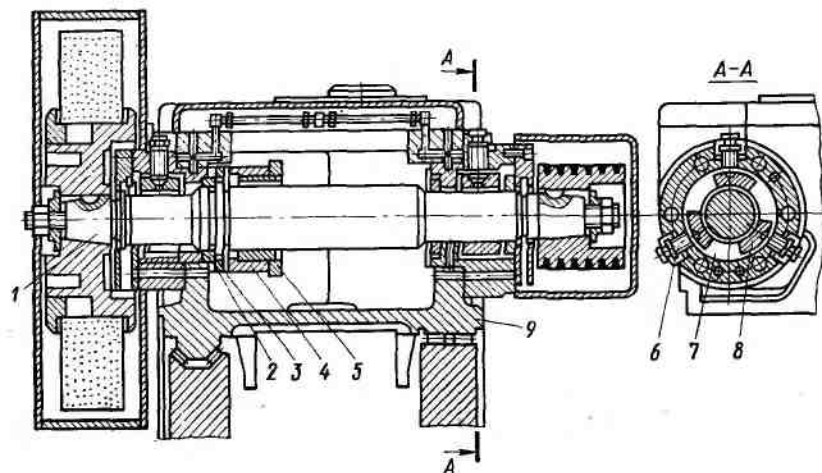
Конструкция шлифовальной бабки круглошлифовального станка мод. 3М151
